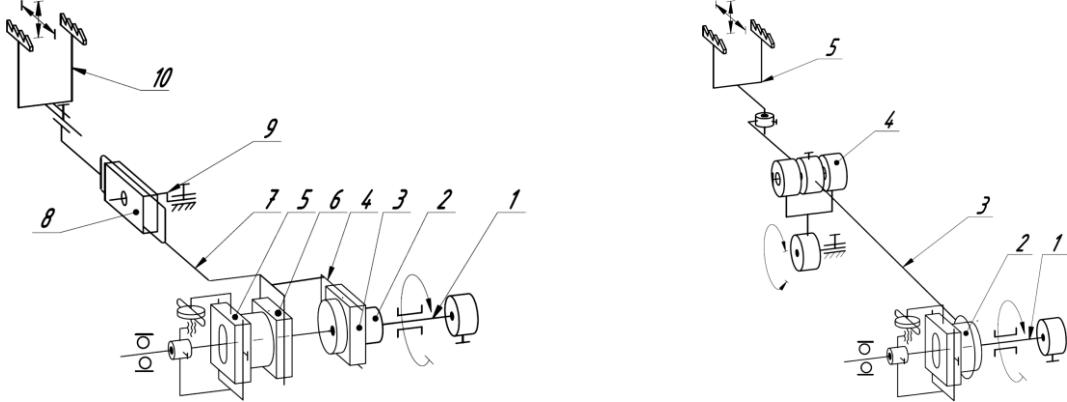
Кінематичні схеми механізмів з зубчастої рейки:
